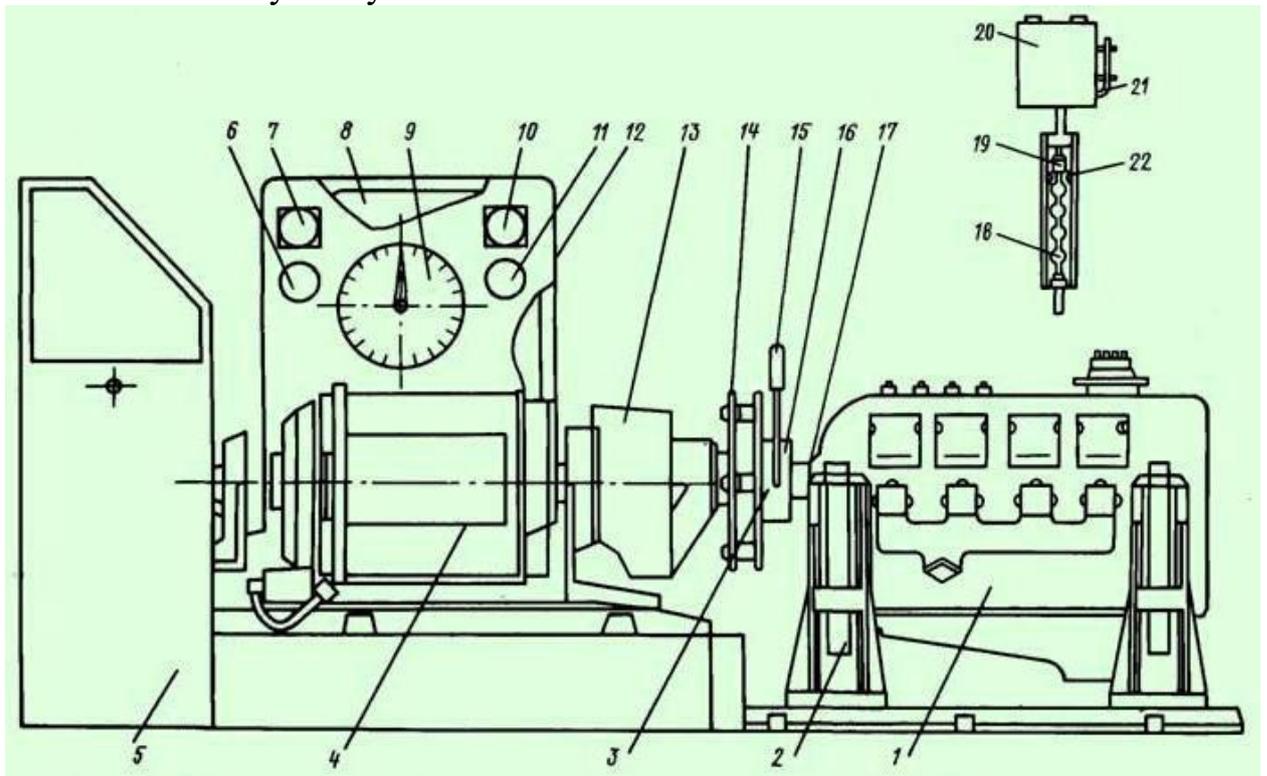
Стенд для обкатки и испытания двигателей
